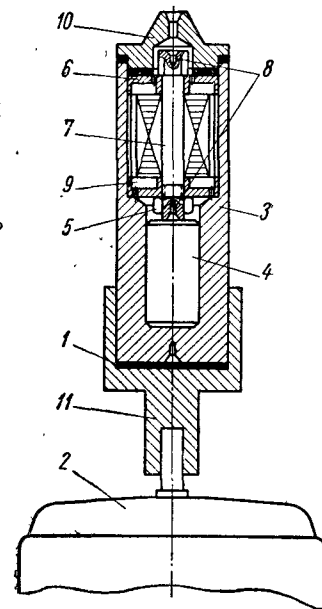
Кокиль для центробежной заливки меди ротора электродвигателя:
